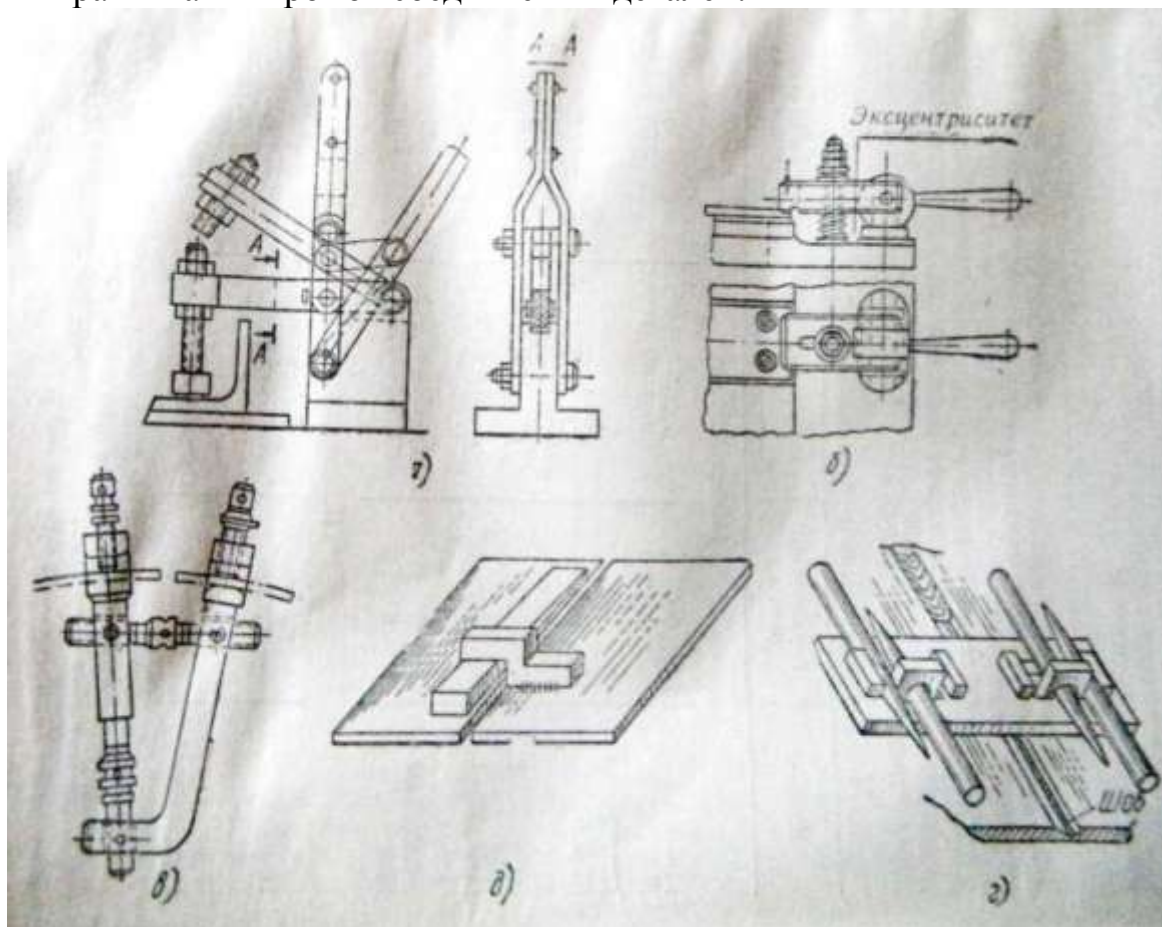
Переносные приспособления для сборочно-сварочных работ.
